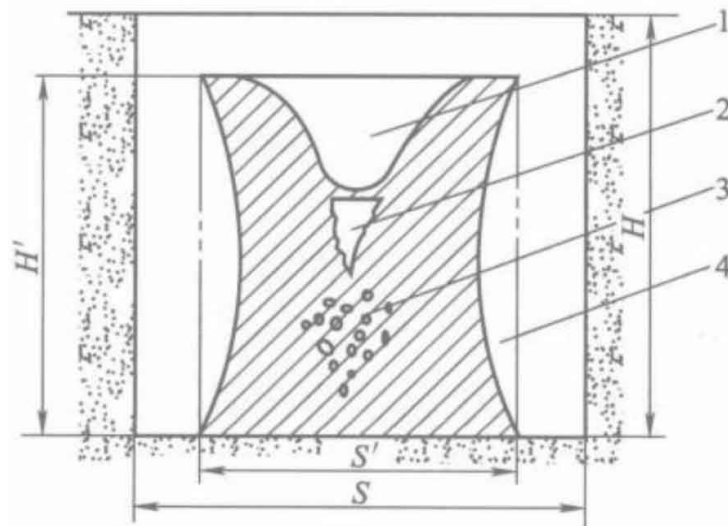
Схема розміщення усадкових дефектів виливка 1- зовнішня усадкова порожнина; 2 – внутрішня усадкова порожнина; 3 - усадкова пористість; 4 – усадкова утяжина бокової поверхні виливка (H – висота робочої порожнини всередині ливарної форми, H^1 – висота виливка після охолодження, S – ширина робочої порожнини всередині ливарної форми, S^1 – ширина виливка після охолодження)
